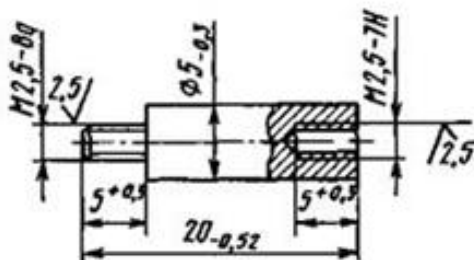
Удлинитель для ножки индикатора при измерении радиальных зазоров с использованием седлообразного приспособления
